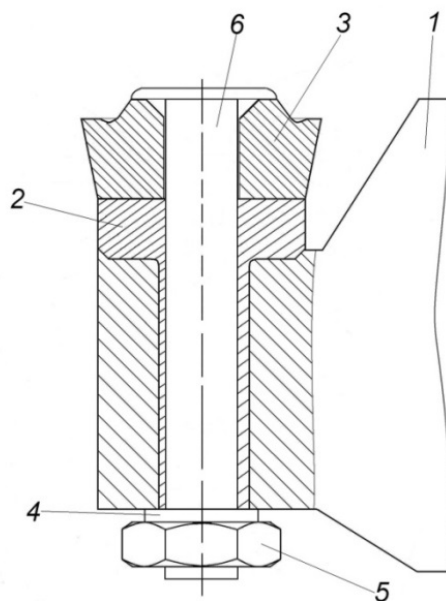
Схема конструкции сборного чашечного резца
